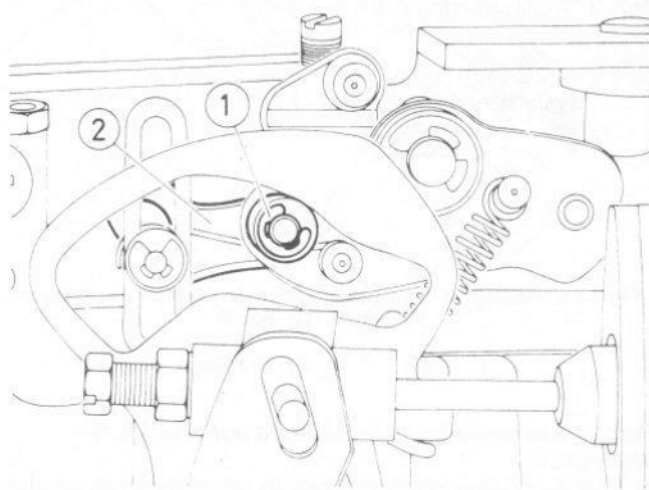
Réglage de l'OVAD - carburateur Weber 36 TLC (Sec 8)
